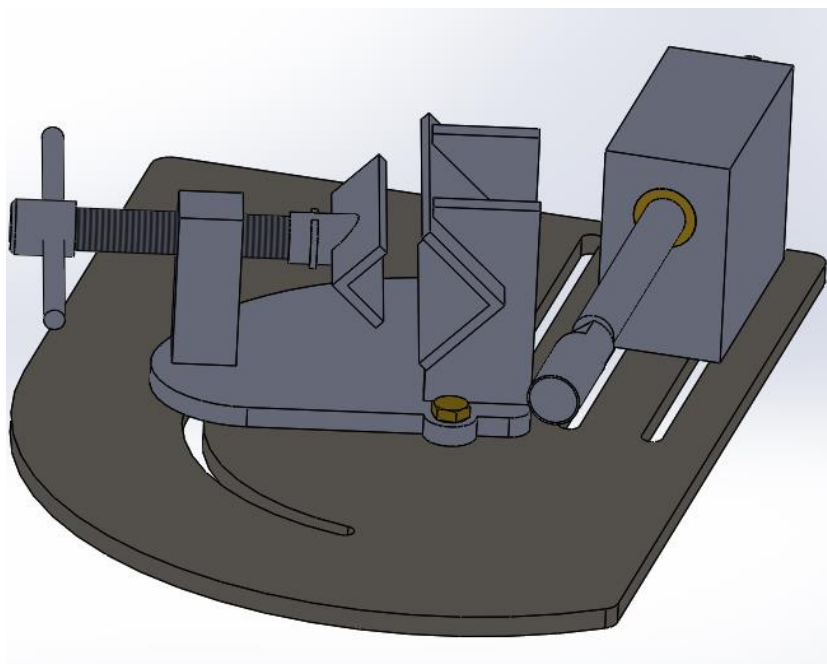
Desenho CAD de Buchas para alívio de atrito com o eixo rotativo
